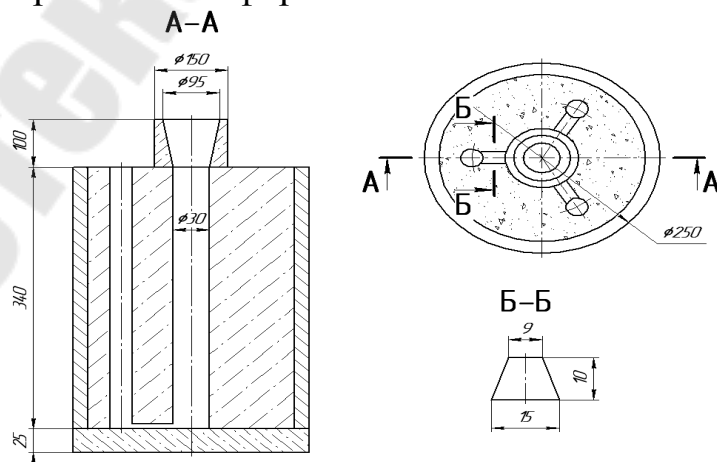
Форма для заливки образцов для механических испытаний
